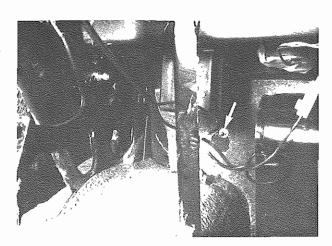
Tirante di fissaggio superiore Upper fixing rod
